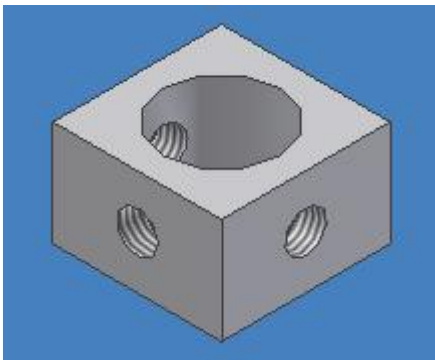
Pieza A6 . Se observa el mecanizado aplicado a 48 piezas según el plano AND00 - 0900
